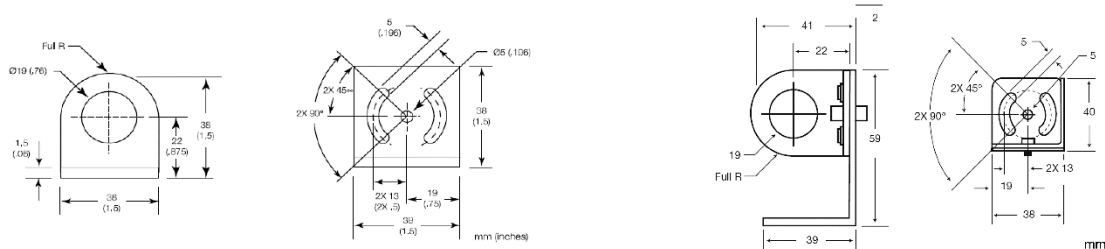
starrer Montagewinkel justierbarer Montagewinkel
